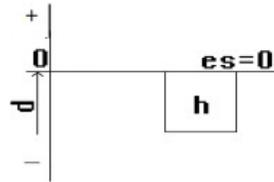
Схема расположения поля допуска основного вала
